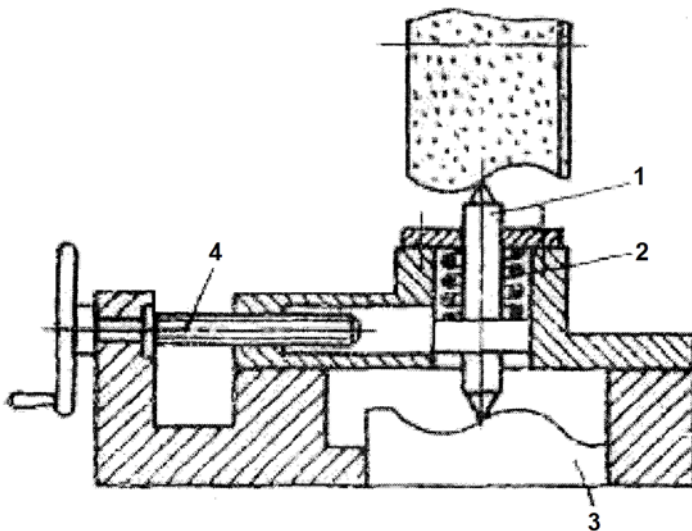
Схема копировального приспособления для профилирования круга
